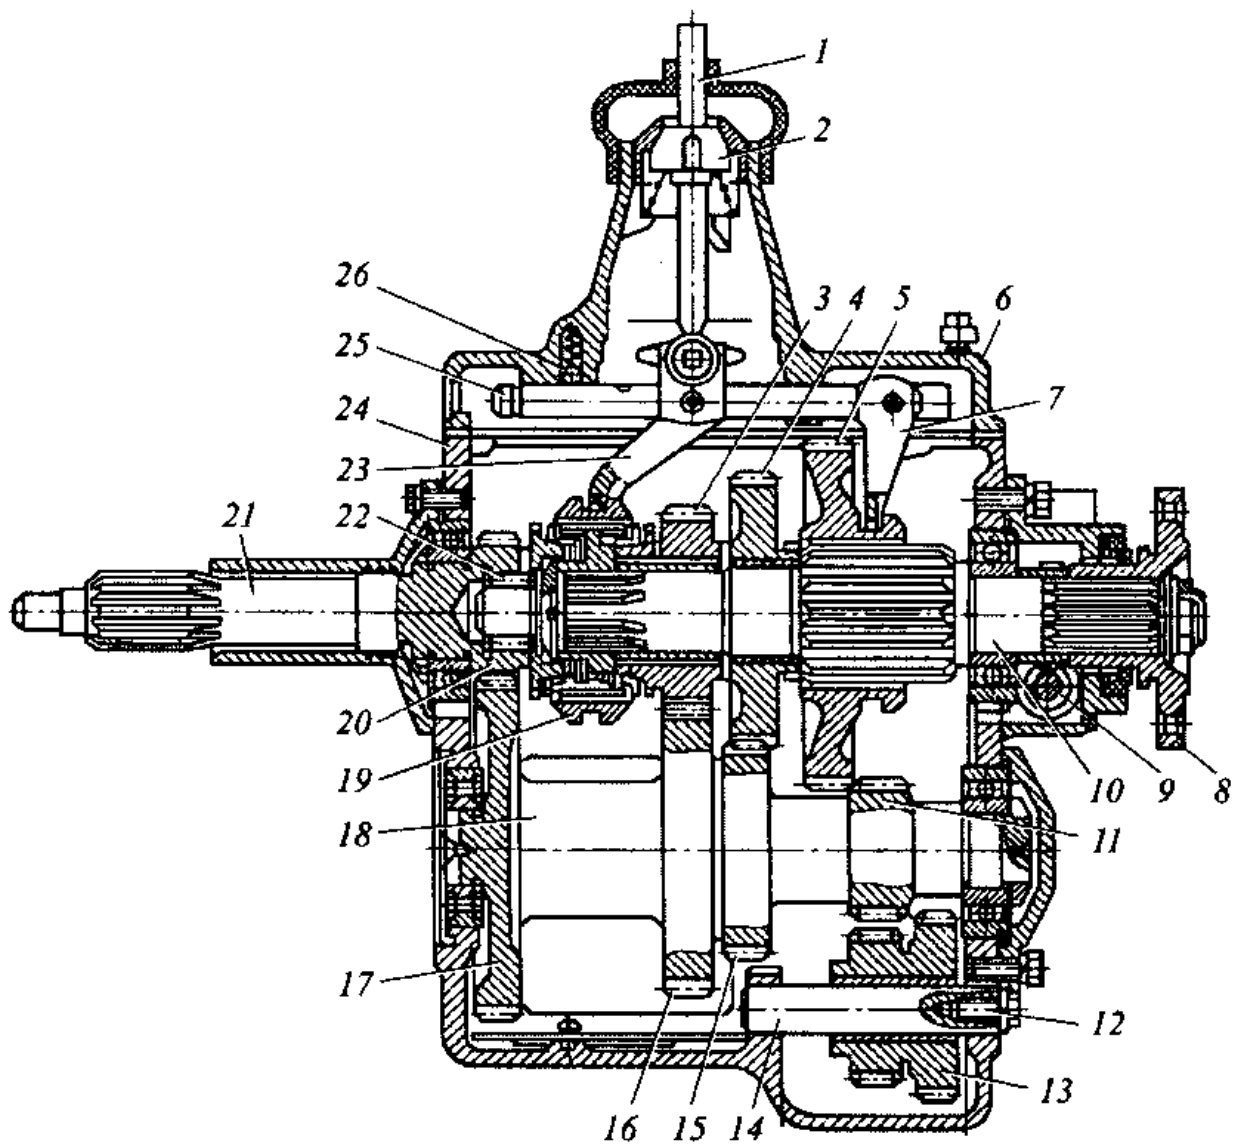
Коробка передач автомобіля ГАЗ-3307:
